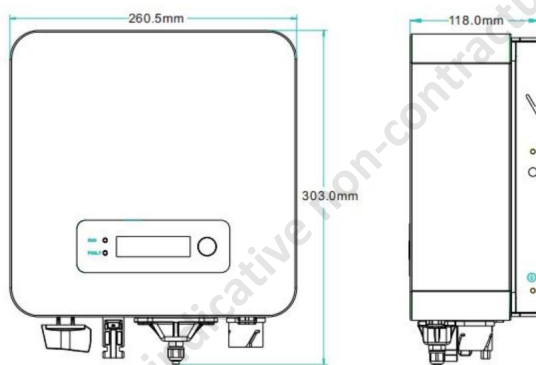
Dimensions de la vue avant et de la vue gauche du SOFAR 3300TL-G3
